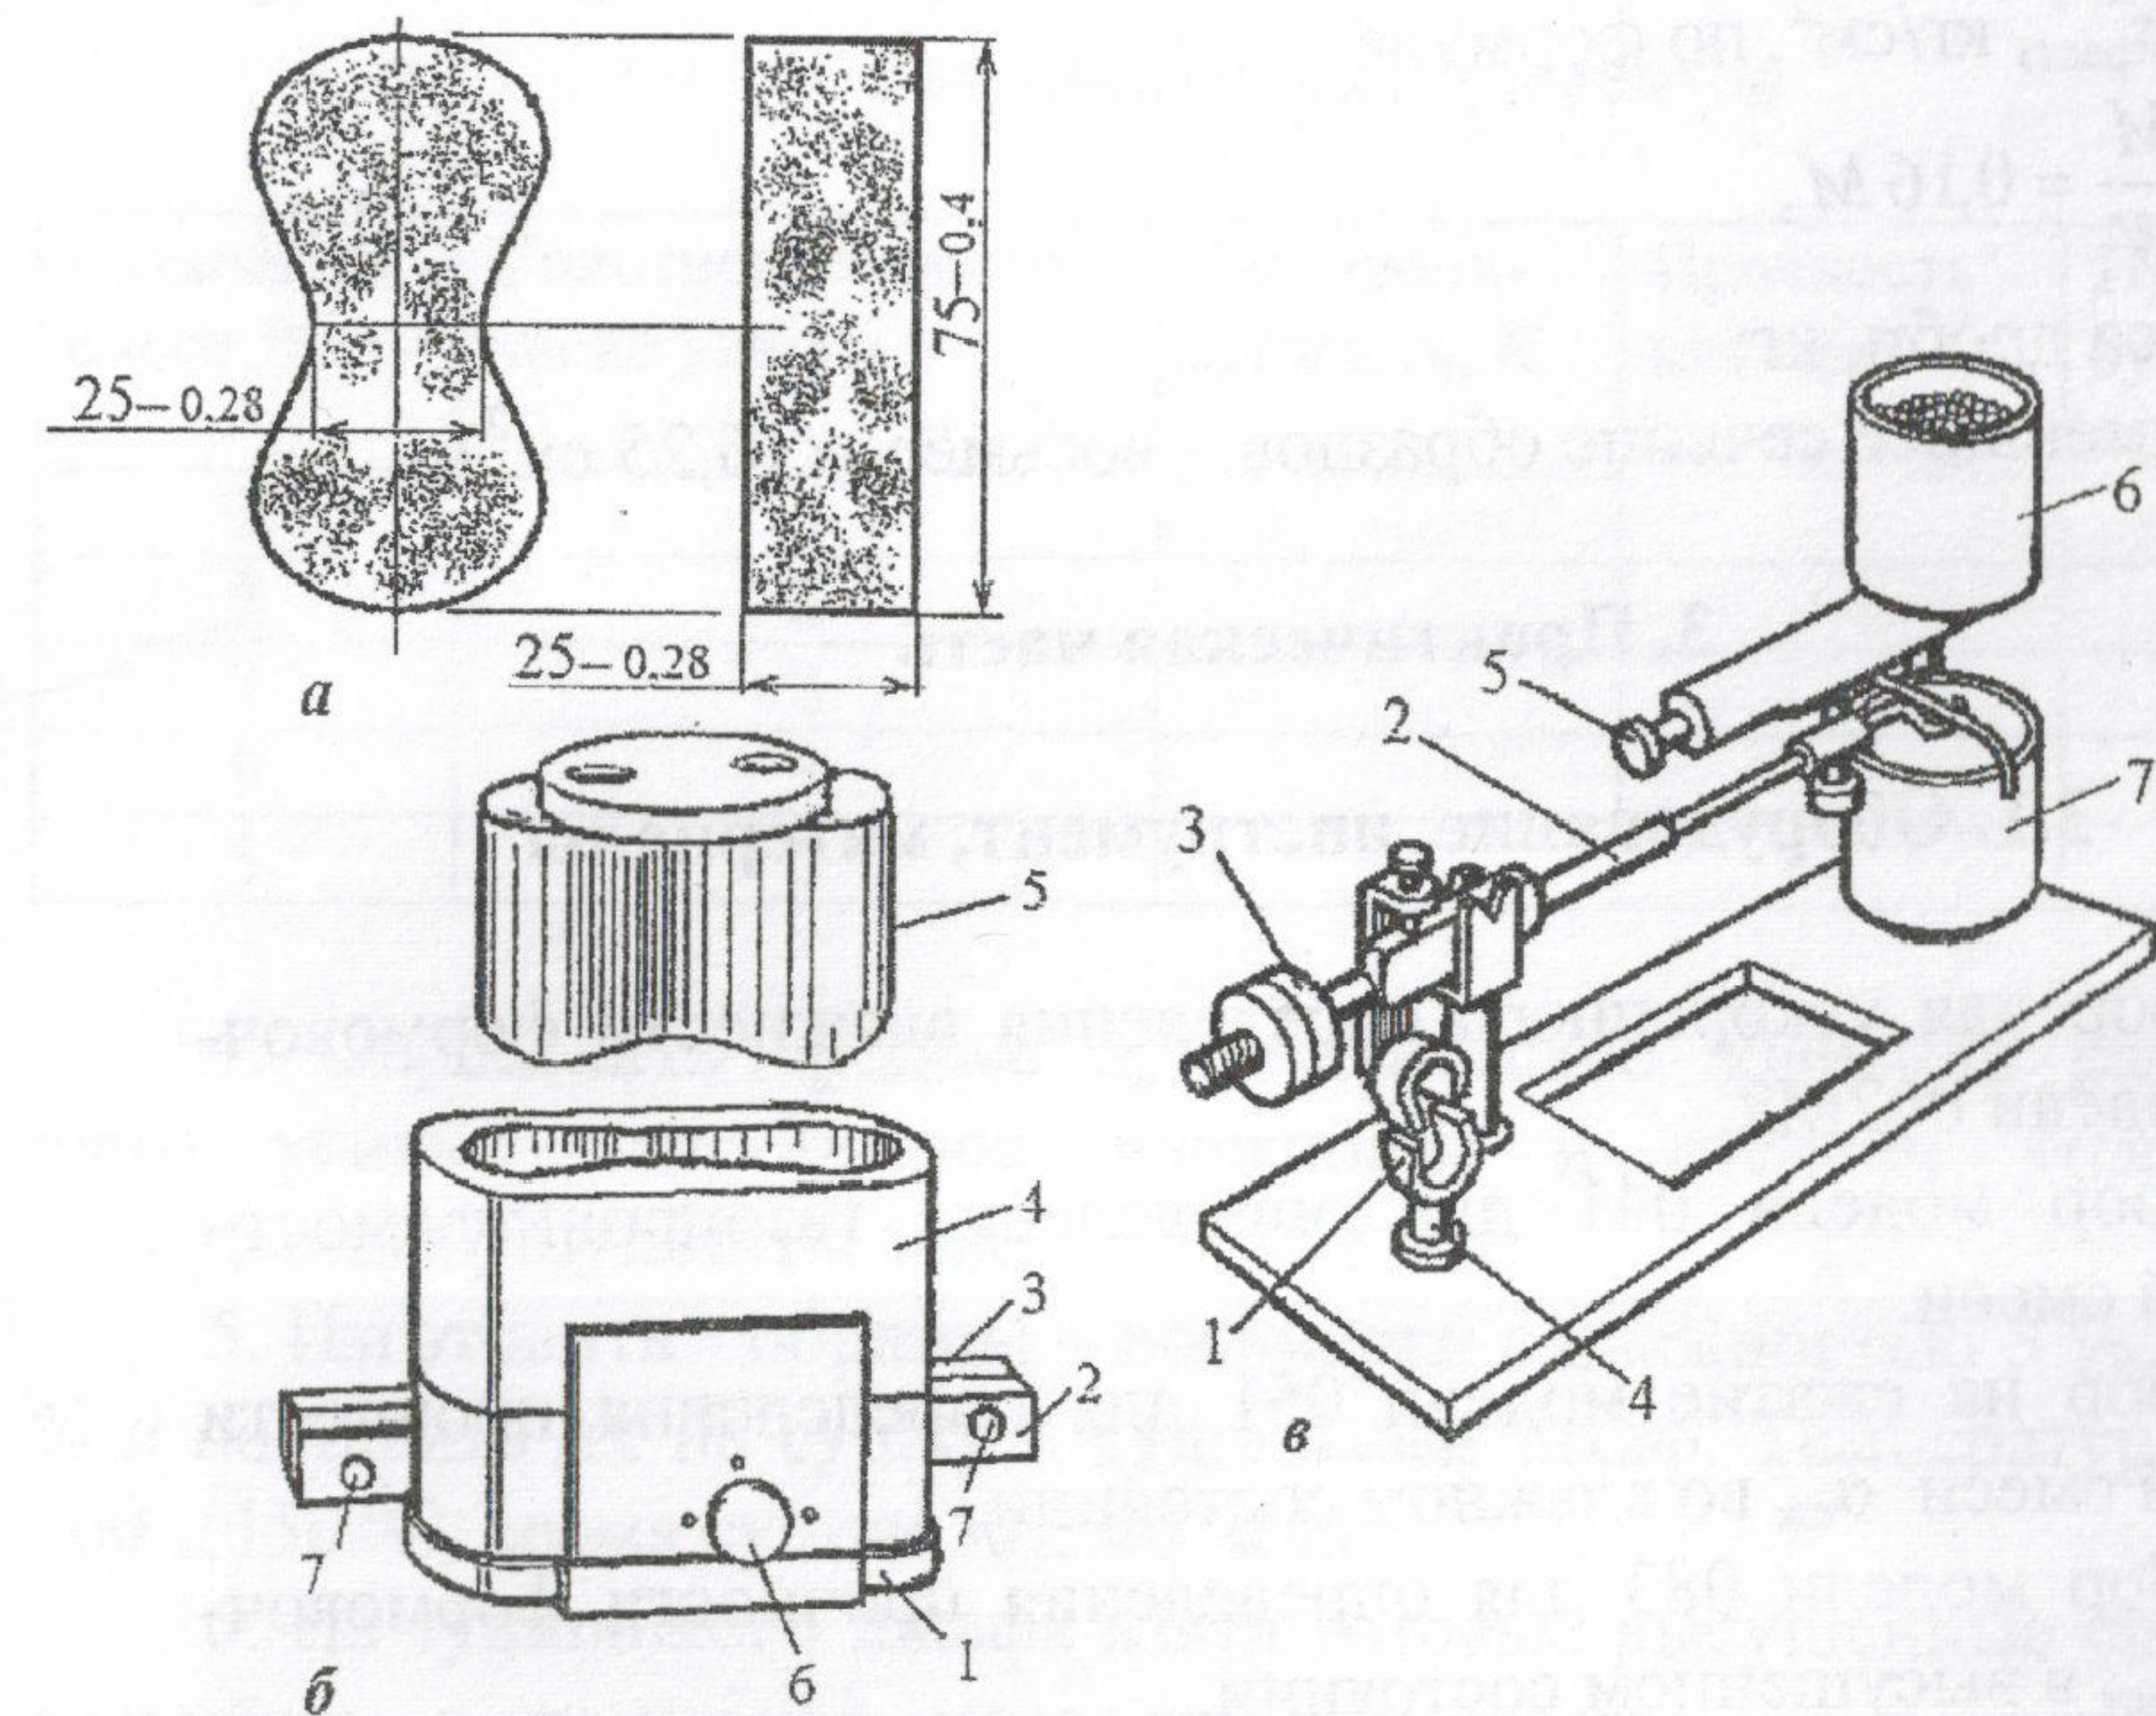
Испытание сухой формовочной смеси на растяжение: *a* – образец-восьмёрка для испытаний; *б* – приспособление (металлический стержневой ящик) для изготовления образцов: 1 – поддон; 2, 3 – половинки формы; 4 – воронка; 5 – колодка; 6 – винт; 7 – штыри; *в* – прибор модели 083 М для определения предела прочности при растяжении  $\sigma_{\text{раст}}$  сухих образцов: 1 – зажим или захват; 2 – рычаг; 3 – груз; 4 – гайка; 5 – затвор; 6 – бункер с чугунной дробью; 7 – ведёрка с навеской дробью.
